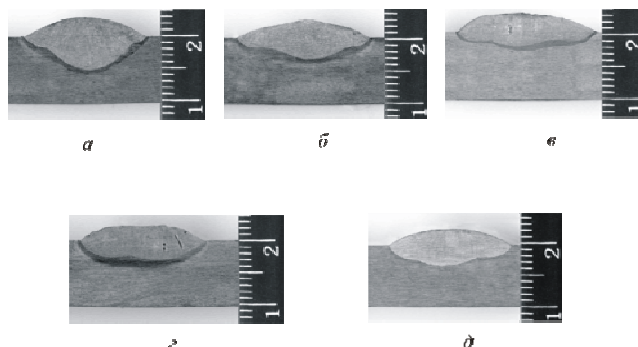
Макрошлифы наплавленных валиков, выполненных при неизменной скорости подачи проволоки: а – $z - z$ – проволока Св-08А и пластина из малоуглеродистой стали ($I_n = 500...550$ А; $U_d = 30...32$ В); б – проволока и пластина из немагнитных материалов; а – наплавка без ПРМП; б – ПРМП частотой 50 Гц, $B_z = 90$ мТл; в – то же, $B_z = 150$ мТл; г – постоянное ПРМП $B_z = 111$ мТл; д – ПРМП частотой 50 Гц, $B_z = 70$ мТл
